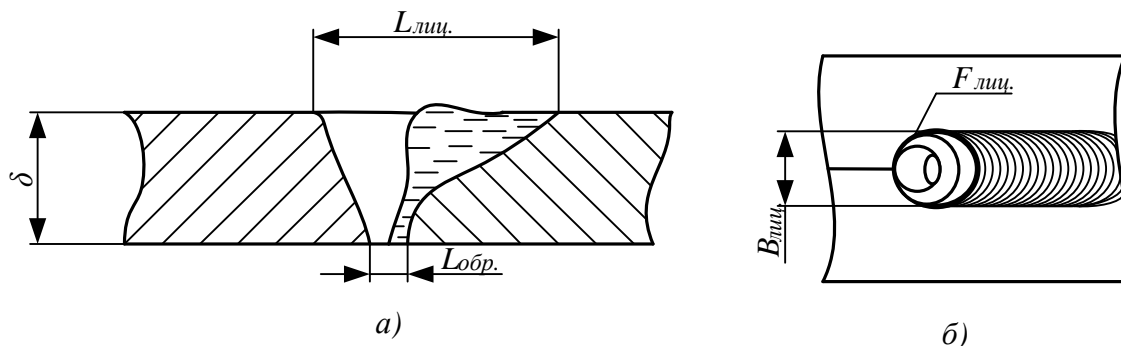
Схема сварочной ванны при сварке со сквозным проплавлением: а – продольное сечение; б – вид сверху.
